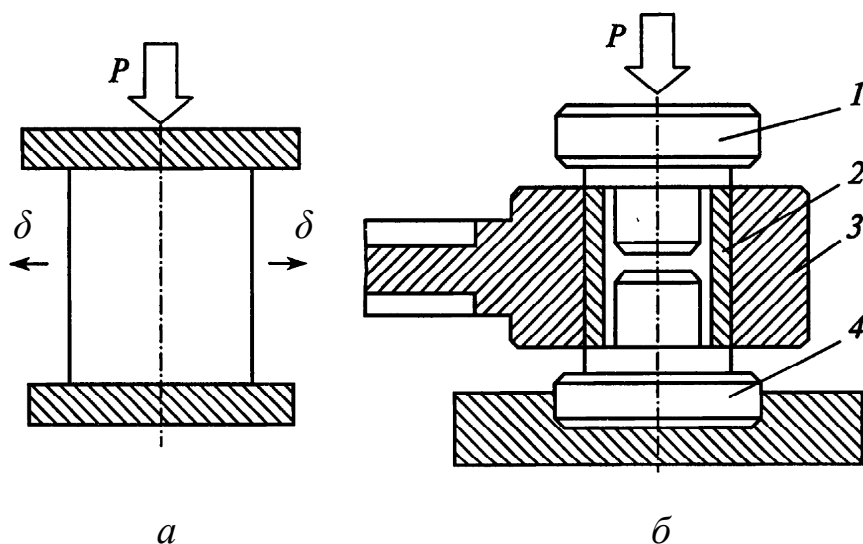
Пластическое деформирование осадкой: а – принципиальная схема; б – осадка давлением втулки верхней головки шатуна; 1, 4 – оправки; 2 – втулка; 3 – шатун
